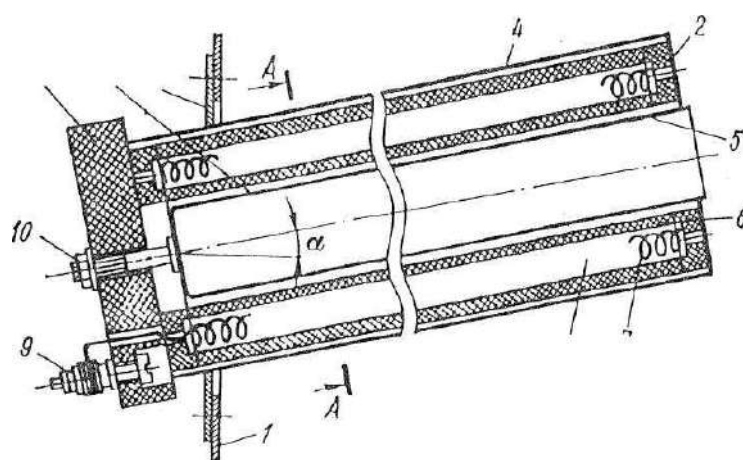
Электронагреватель масла с увеличенной поверхностью теплопередачи: 1 – крышка; 2 – заглушки; 3 – фланец корпуса; 4 – корпус; 5 – труба; 6 – изолятор; 7 – спираль; 8 – каналы; 9 – контактный винт; 10 – винт крышки.
